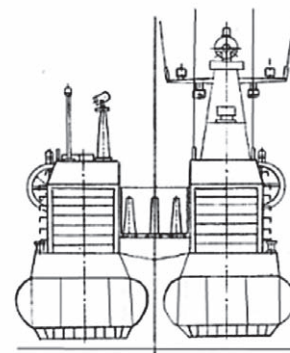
Конструктивная схема двухкорпусного НАВП (вид спереди) с расположением подъемно-двигательного комплекса с ВИШ (ВФШ) в кольцевых насадках, осевыми нагнетателями и сквозной открытой грузовой палубой
